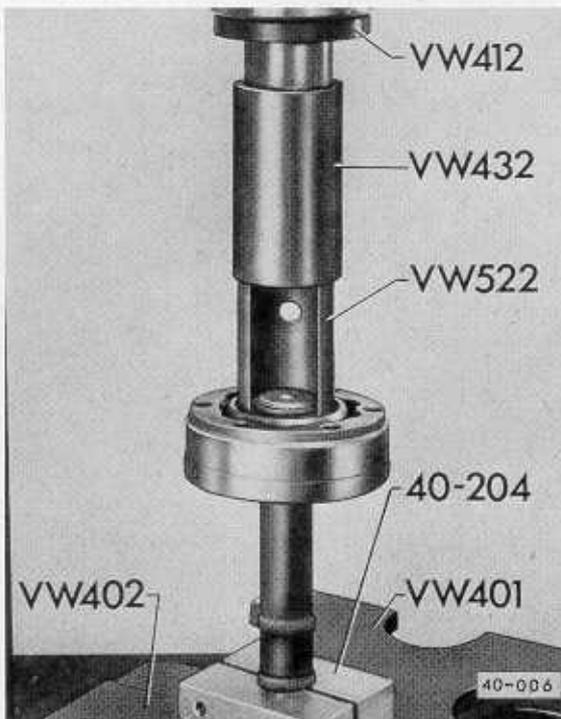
Gleichlaufgelenk auf die Welle aufpressen und gleichzeitig Sicherungsring in die Nut einsetzen.
